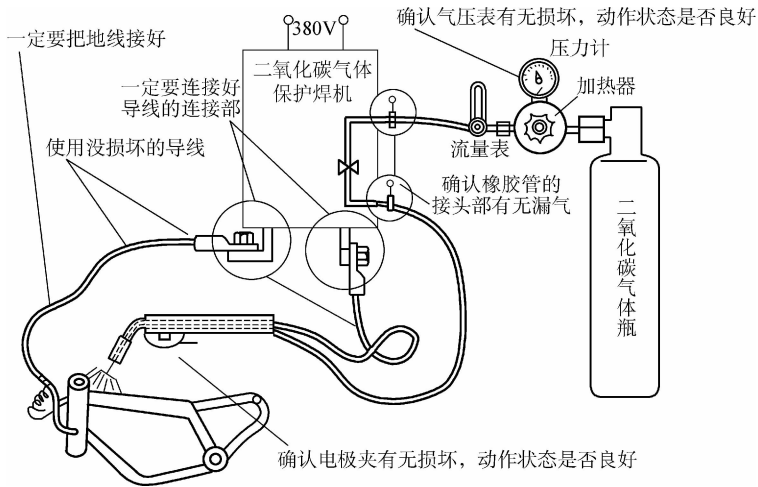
二氧化碳气体保护焊机日常保全的要点
